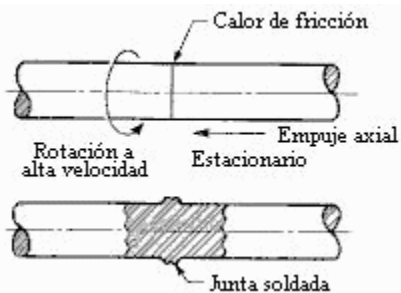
Ilustración de un proceso que emplea calor generado por fricción para producir una soldadura
